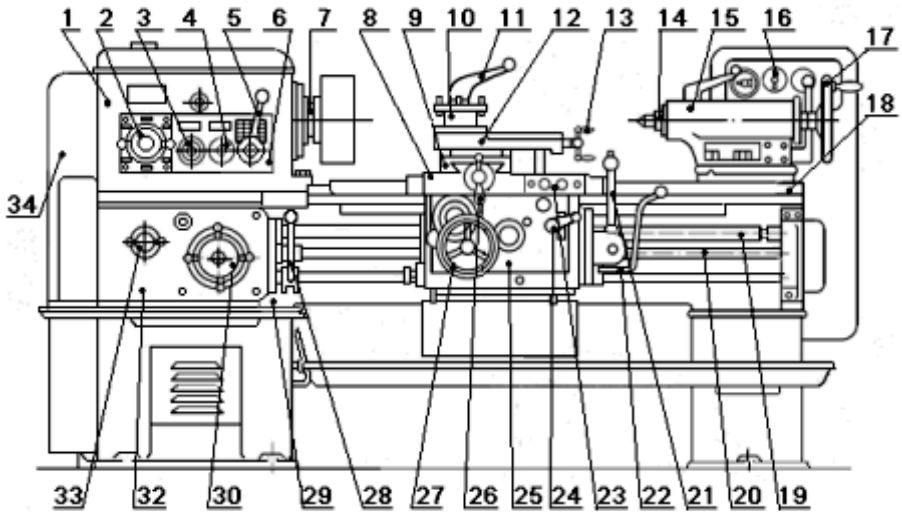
Токарно-винторезный станок 1К62: 1 – передняя (шпиндельная) бабка; 2, 3, 4, 5 – рукоятки; 6 – коробка скоростей; 7 – шпиндель; 8 – продольные салазки (каретка); 9 – поперечные салазки; 10 – резцедержатель; 11 – рукоятка; 12 – поворотный суппорт; 13 – рукоятка; 14 – пиноль; 15 – задняя бабка; 16 – переключатель; 17 – маховик; 18 – направляющие станины; 19 – ходовой винт; 20 – ходовой вал; 21, 22 – рукоятки; 23 – кнопки; 24 – рукоятка; 25 – фартук; 26, 27 – маховики; 28 – рукоятка; 29 – станина; 30 – рукоятка; 32 – коробка подач; 33 – рукоятка; 34 – гитара.
